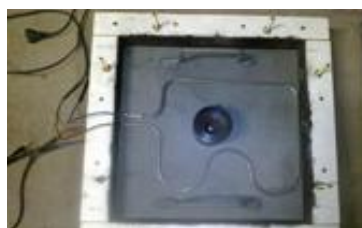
Dispositivo de aquecimento superior do molde desenvolvido
